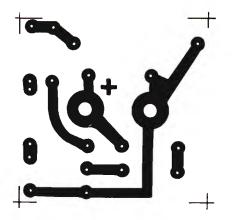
Riportiamo in questo disegno le tracce relative alle piste di rame del circuito stampato che il lettore dovrà riprodurre, in queste stesse identiche dimensioni, per poter realizzare la costruzione del voltmetro per rete-luce. Si tenga presente che le distanze tra i due anelli centrali, destinati ad ospitare i perni filettati dei morsetti del voltmetro, sono quelle standard normalmente adottate in tutti gli strumenti di misura. In caso diverso, il lettore provvederà ad aumentare o diminuire la distanza dei due fori nella misura necessaria. Il foro che va collegato al morsetto positivo dello strumento è quello contrassegnato con la crocetta.
